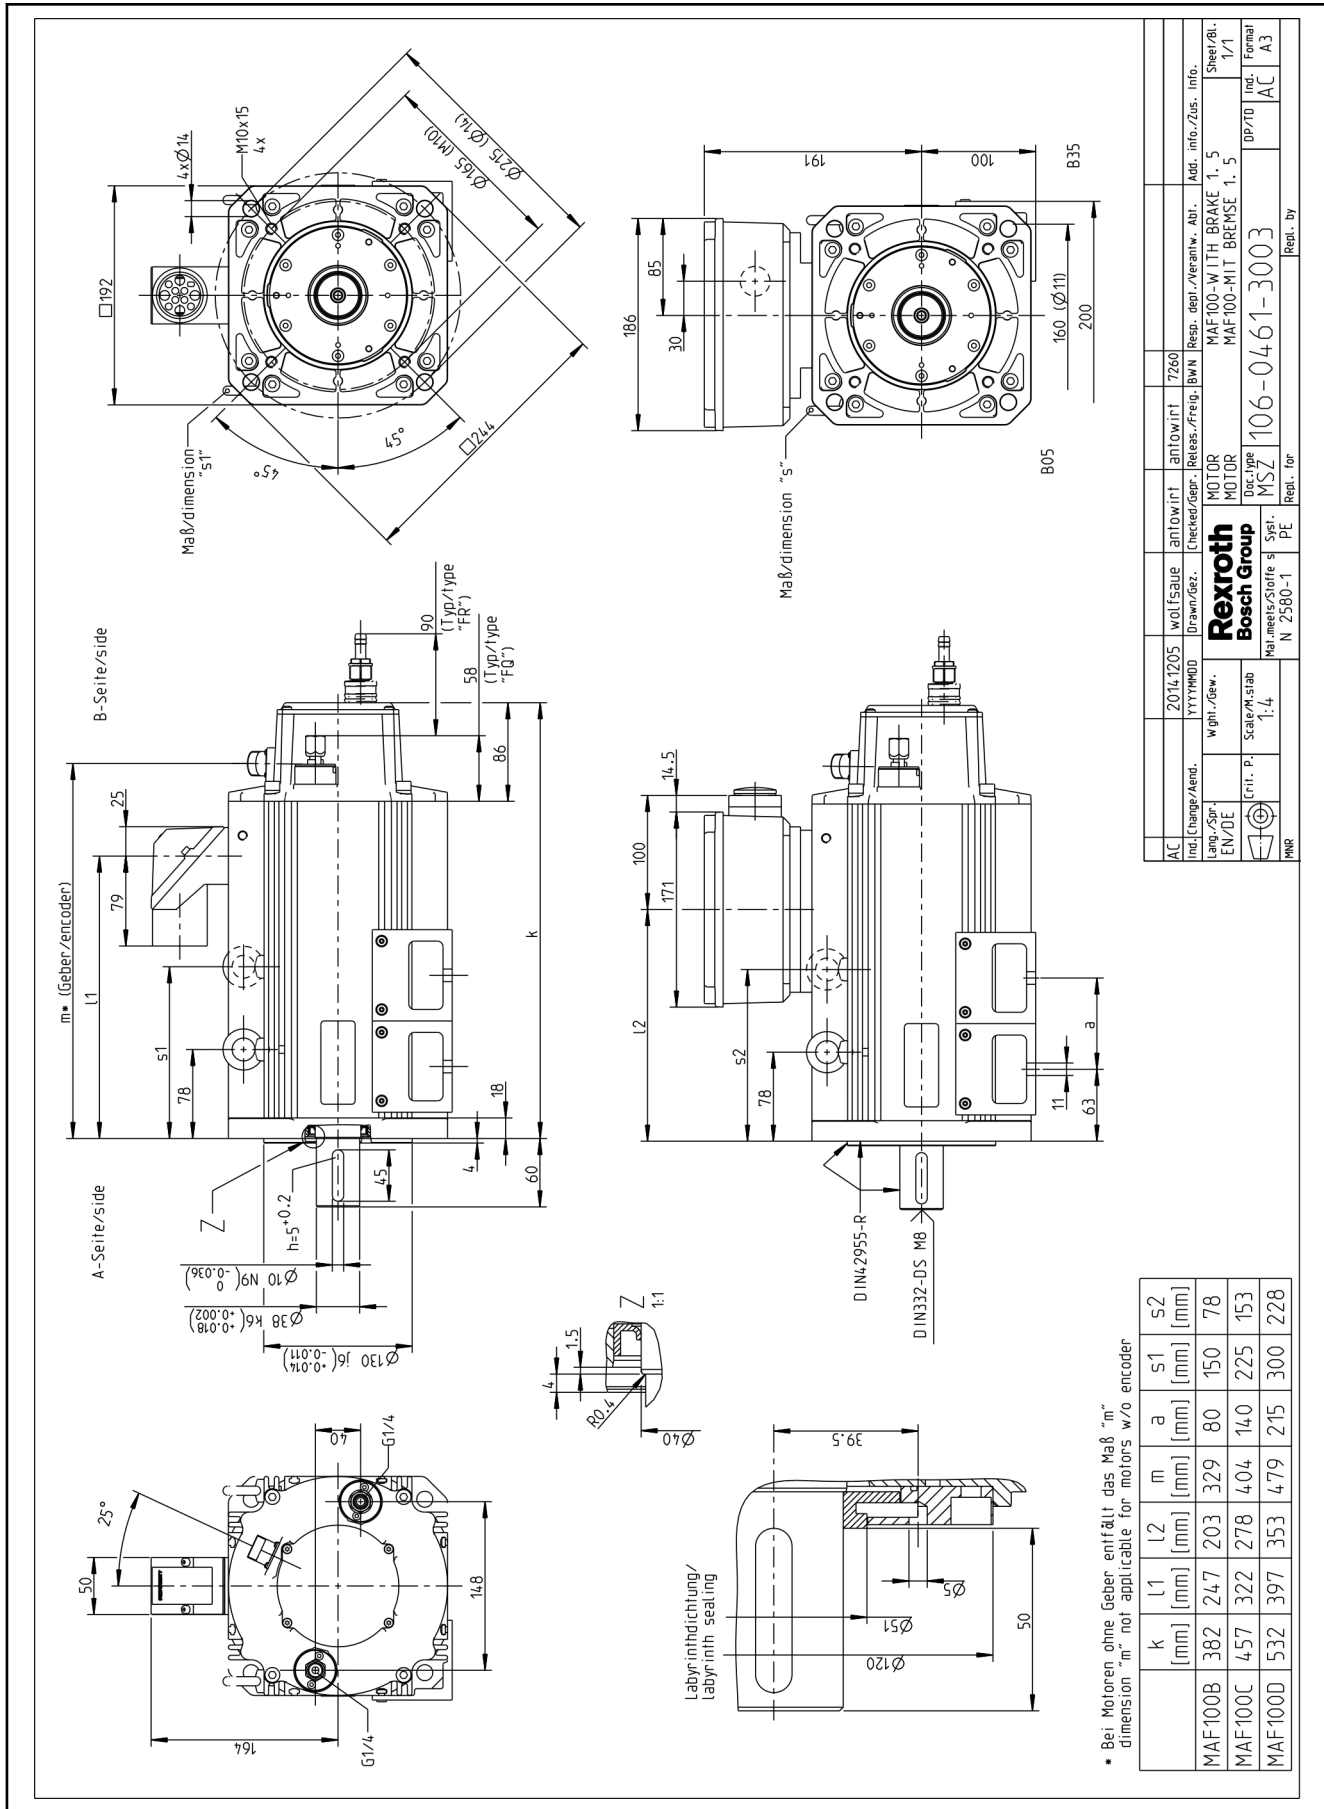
MAF100 mit Bremse 1 oder 5
